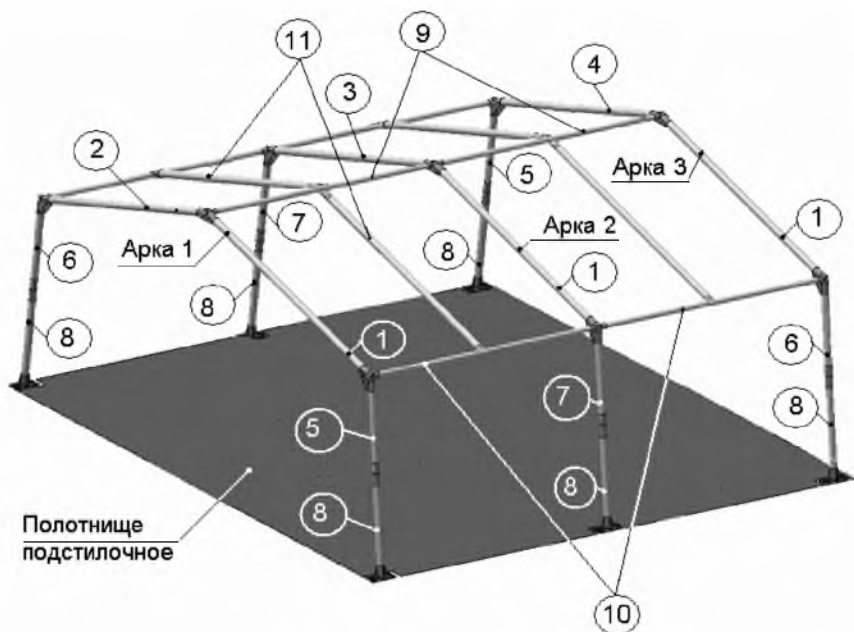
Каркас палатки типа СМ.ПКн с полотнищем подстилочным:
